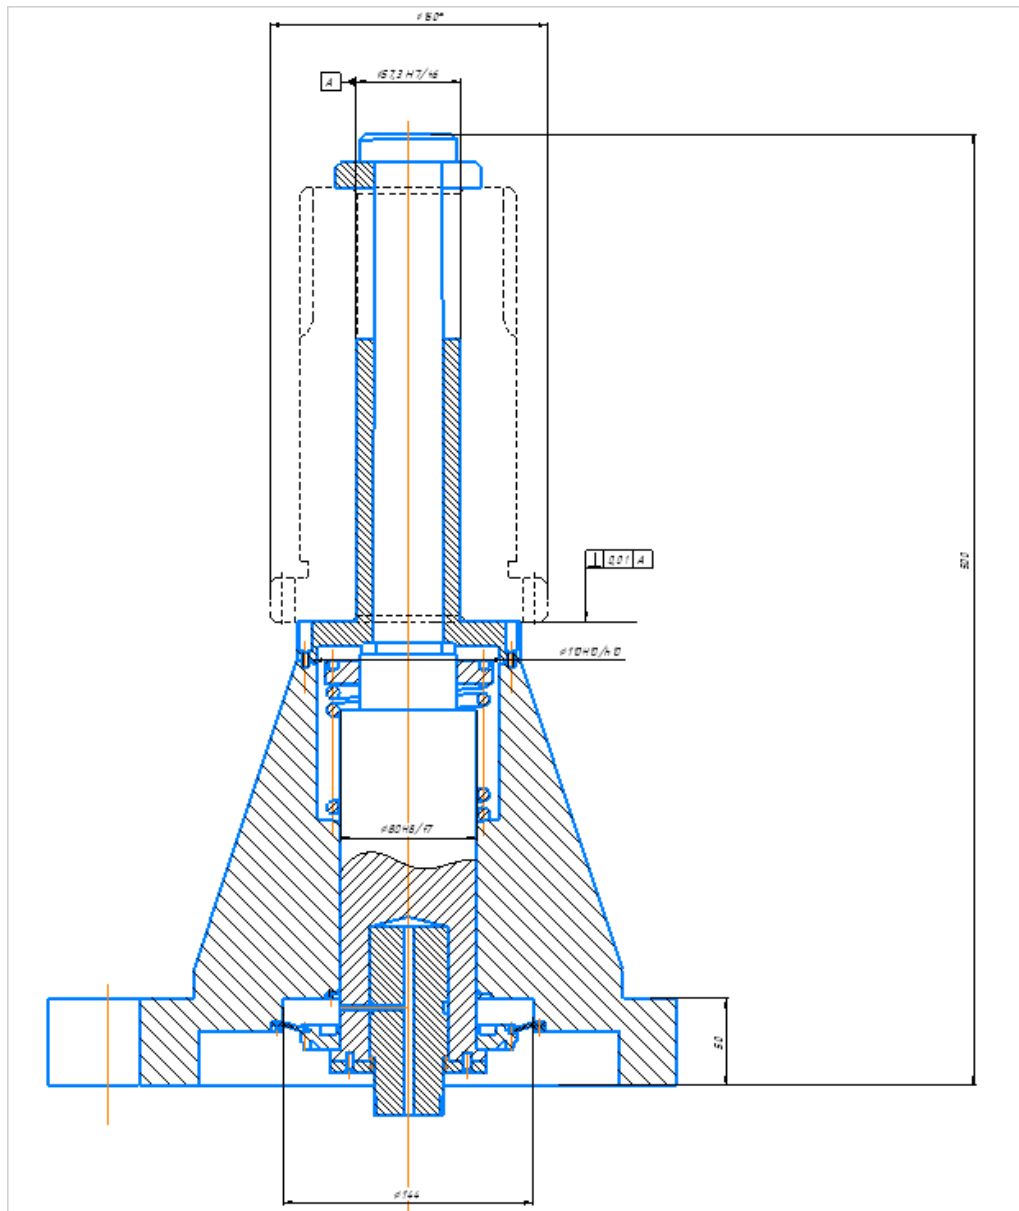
Ескіз пристосування для зубофрезерування
